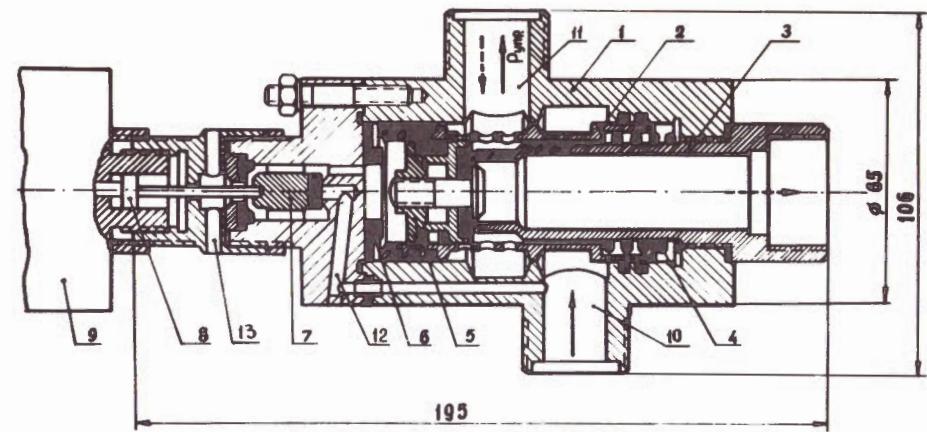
Пневматический усилитель ПУ1, ПУ2: 1 - корпус; 2 - подвижной цилиндр; 3 - выхлопной патрубок; 4 - пружина; 5 - поршень; 6 - демпфер; 7 - пусковой клапан; 8 - шток; 9 - электромагнит; 10 - напорный патрубок; 11 - магистраль $P_{\text{упр.}}$.
